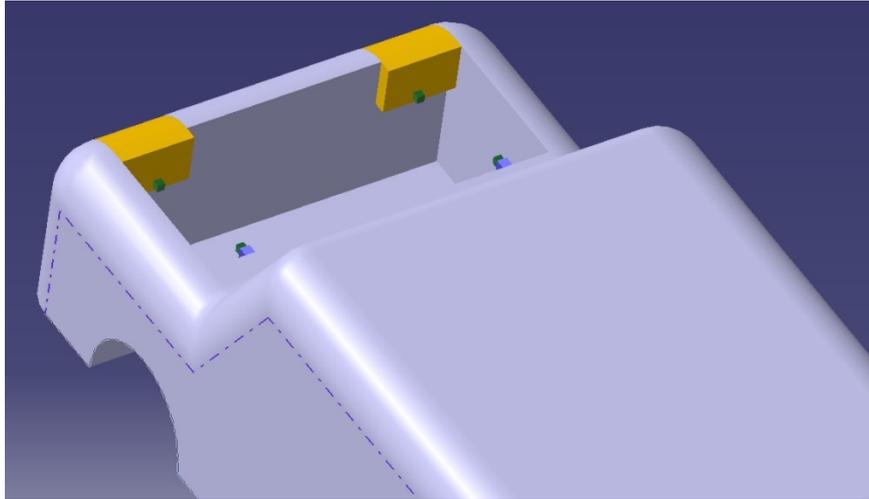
Rückansicht der Scheinwerfer mit Lichtschrankensensoren
